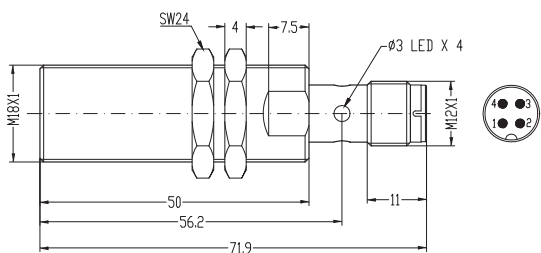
Lange Ausführung, bündiger Einbau, Steckversion
